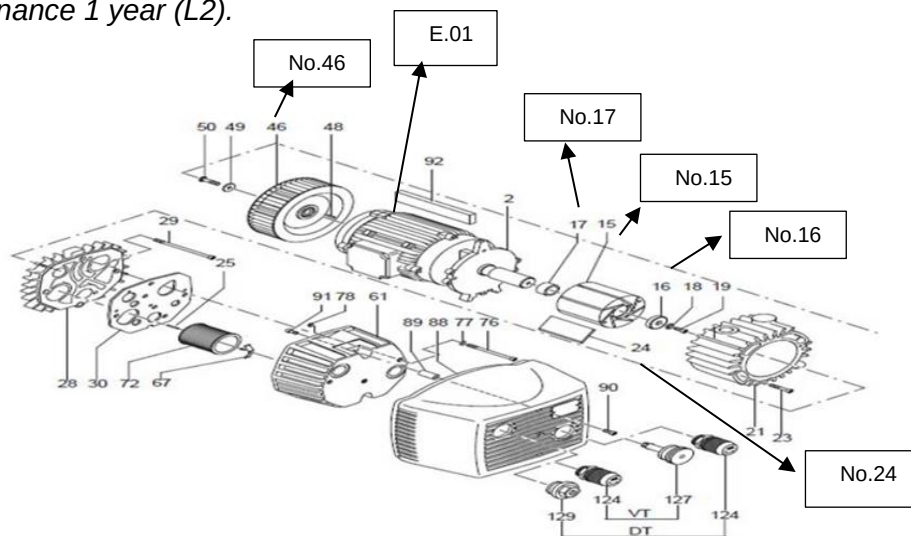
Unit mesin vacuum untuk particle counter mesin filling bosch
